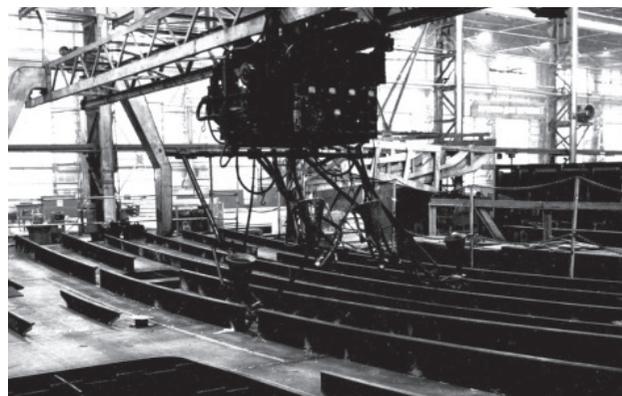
Сварка палубной секции корабля шланговыми автоматами ПШ-5
